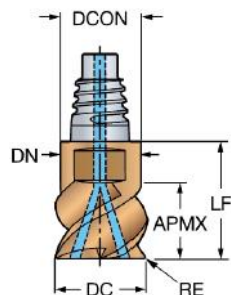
Cap de frezat din carbură metalică A316-25SM550C10032P 1030 [3]
